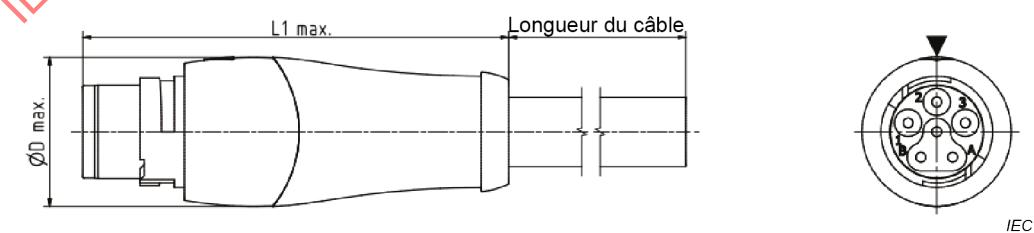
Connecteur démontable, contacts mâles, version coulée
